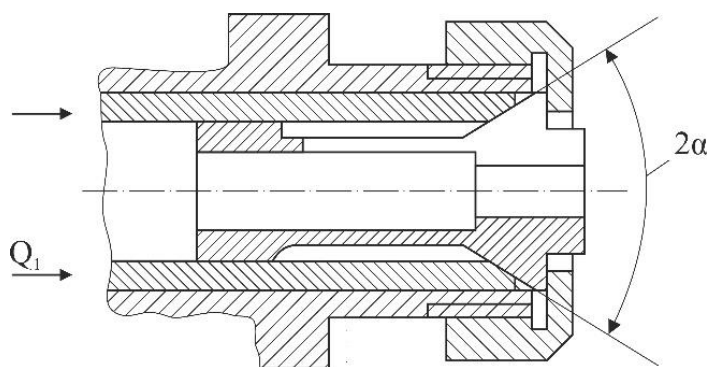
Цанговый патрон для крепления прутков с конусом под цангу в корпусе
